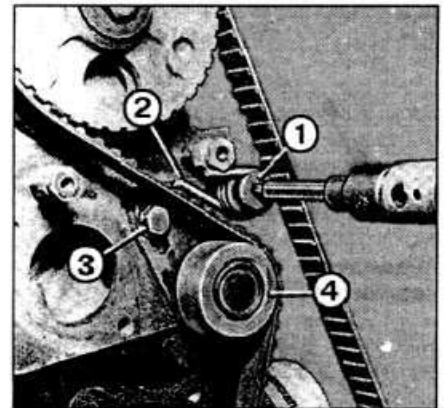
Натяжитель ремня привода распределительного вала:
